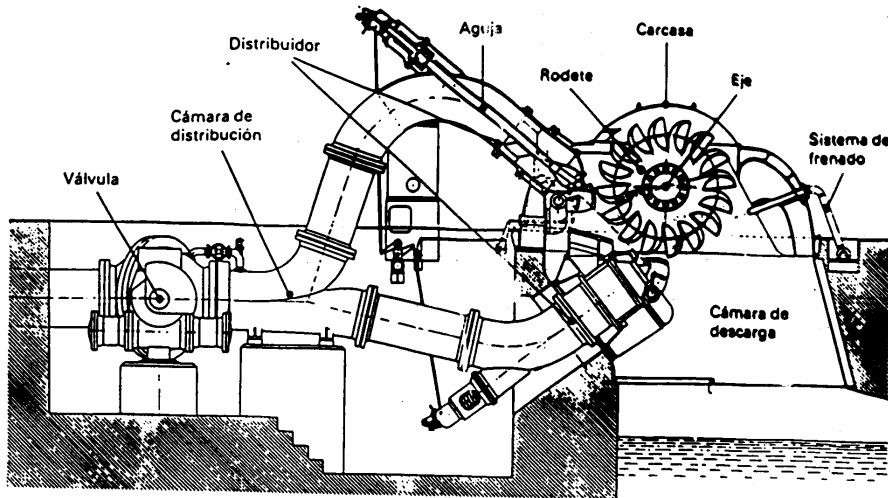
Componentes de una turbina Pelton de eje horizontal, con dos equipos de inyección.
